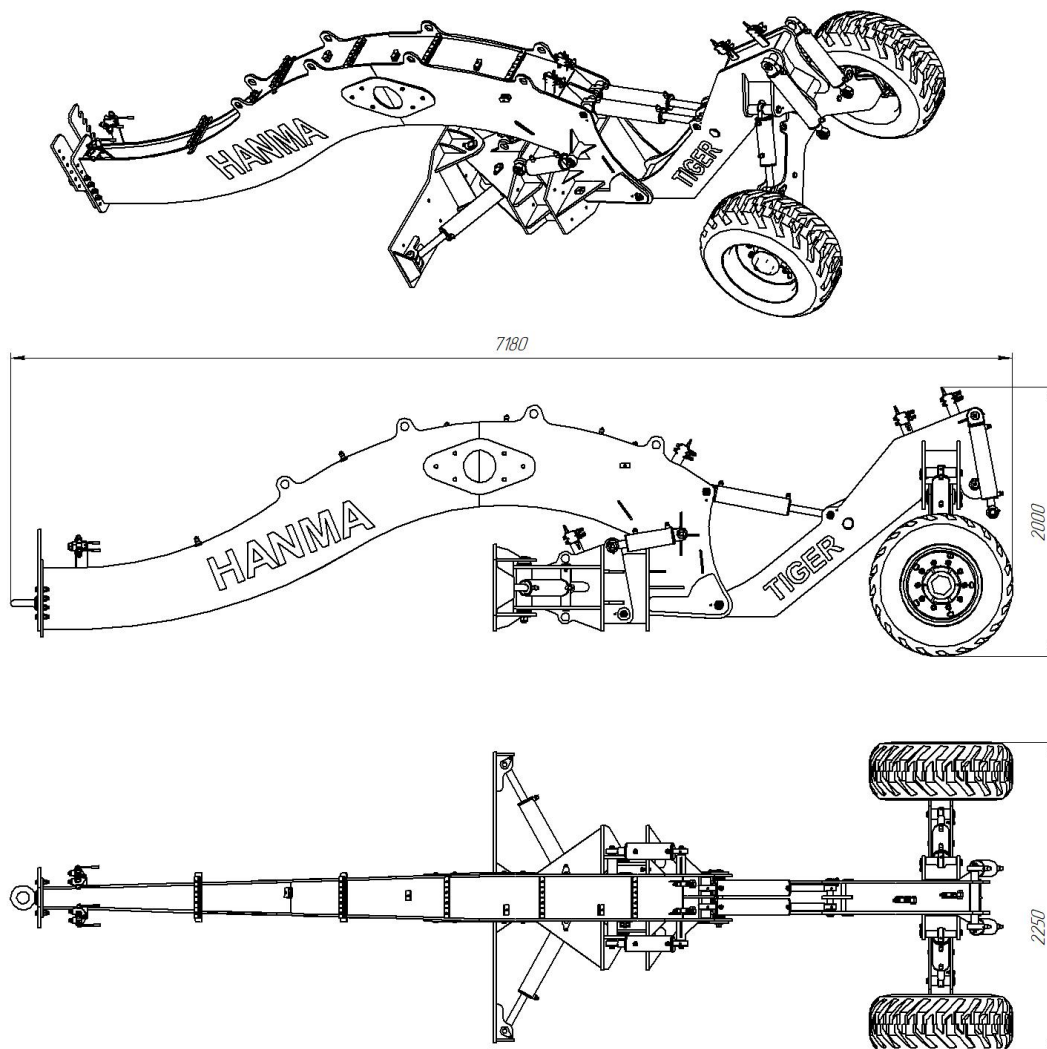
Габариты рамы в сборе с рычагом и сцепкой
